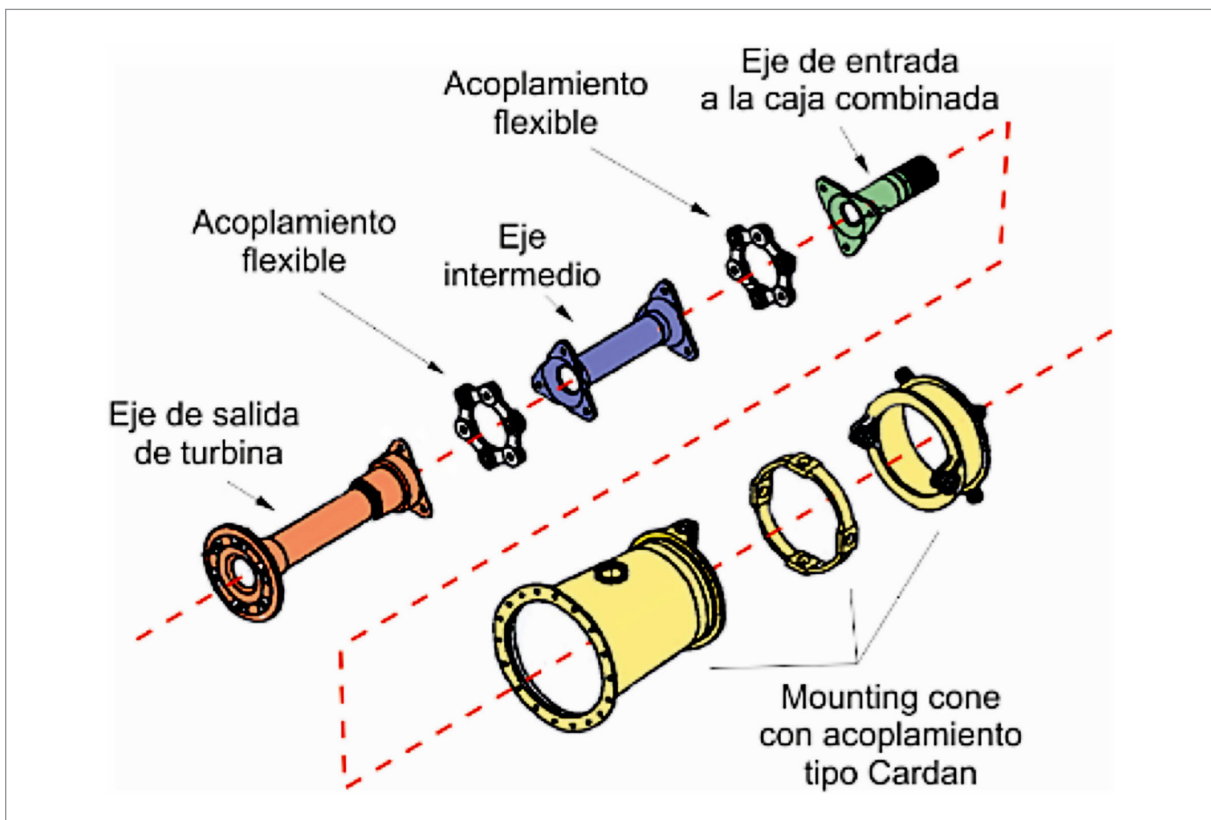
Despiece de las partes que componen el eje de salida de la turbina hasta la caja combinada y su carcasa de recubrimiento (*mounting cone*)
